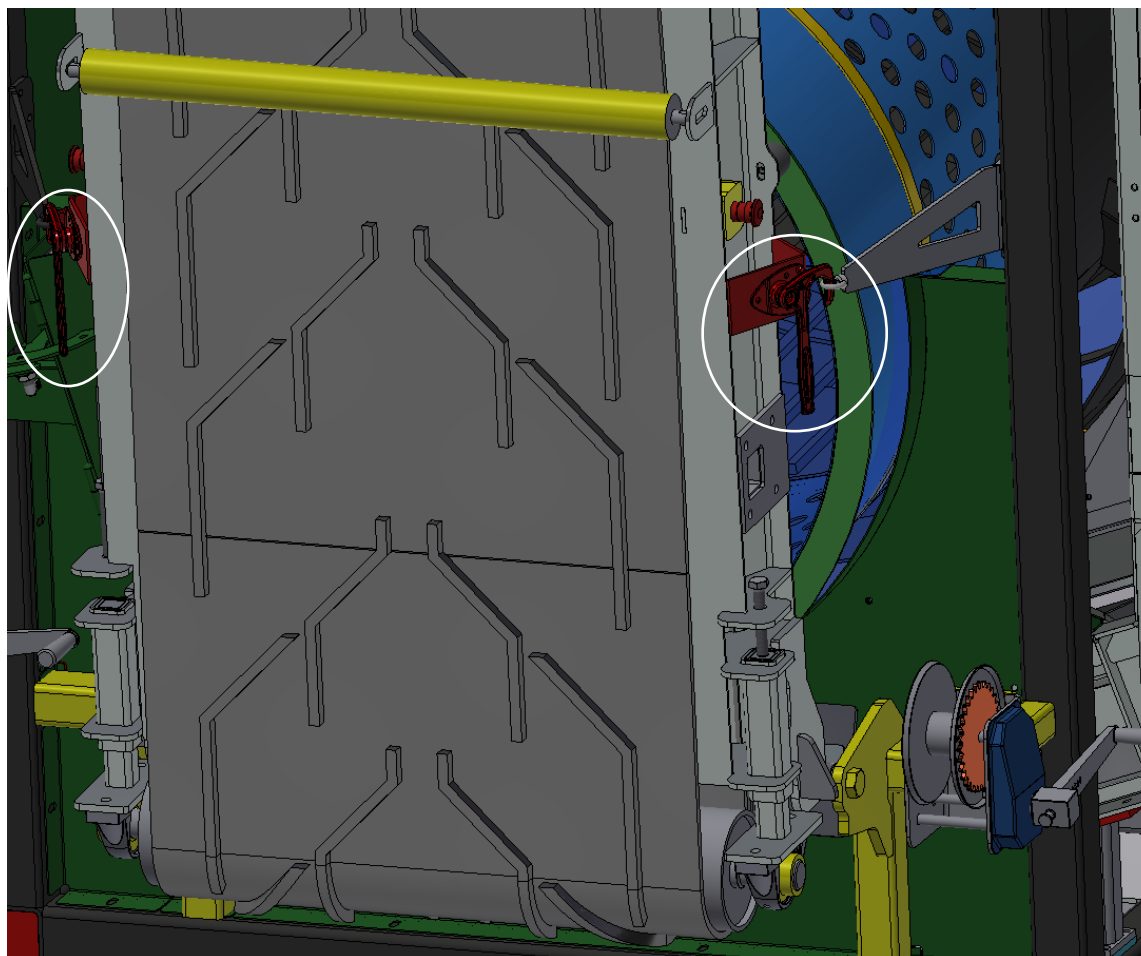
Transportní zajištění jemné / hrubé frakce
